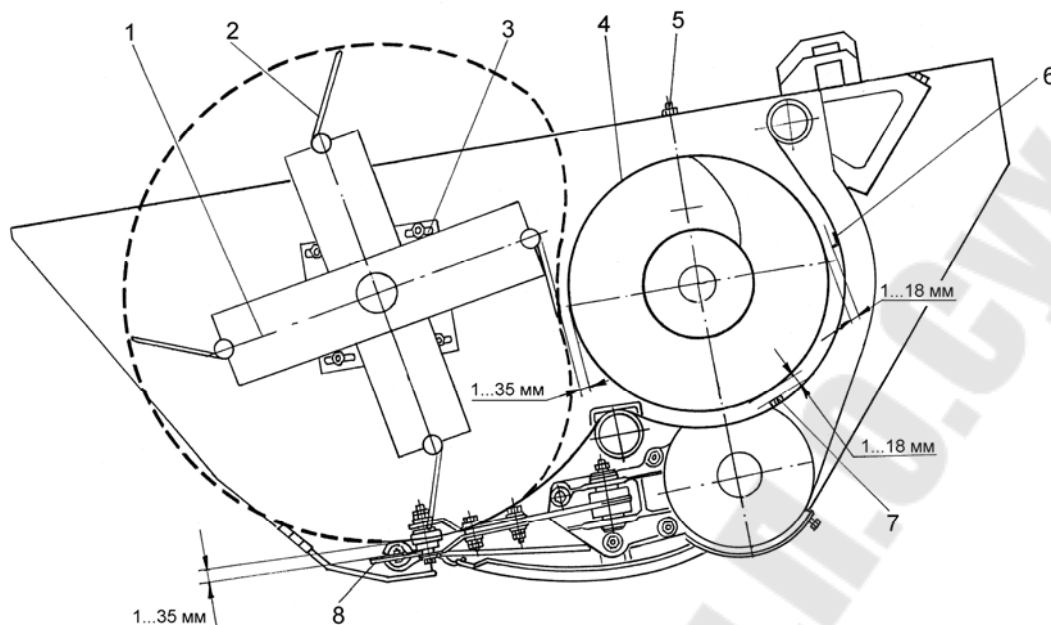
Схема регулировки положения мотовила и шнека жатки для трав:
